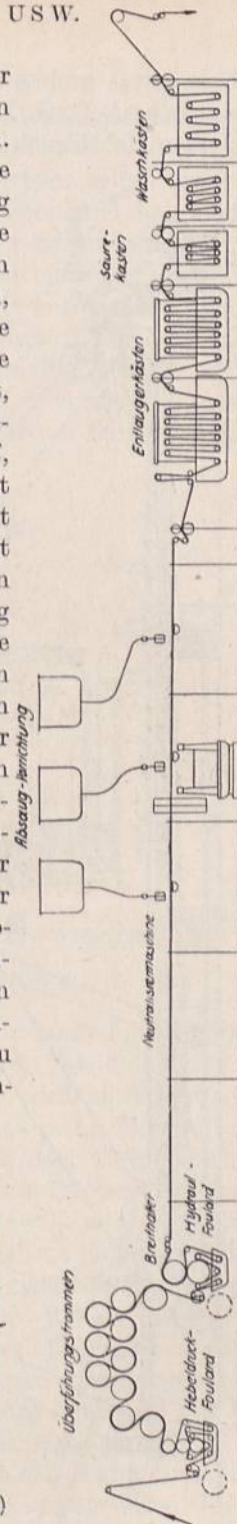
Mercerisier-Anlage mit Kettenspannmaschine. (Haubold.)
